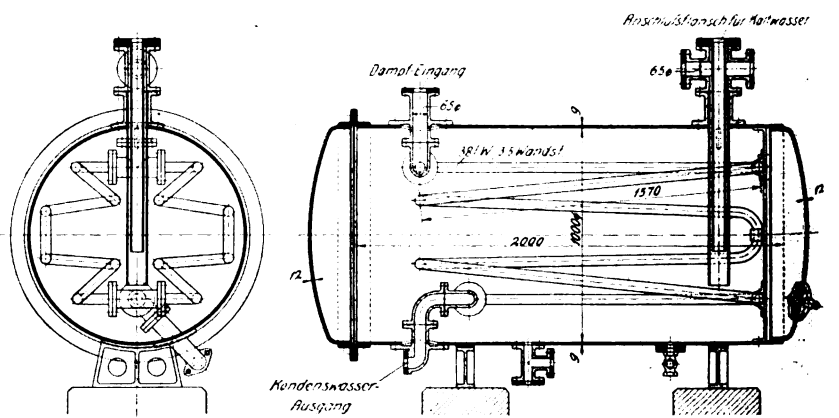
Warmwasserbehälter mit Dampfrohrrschlange.
